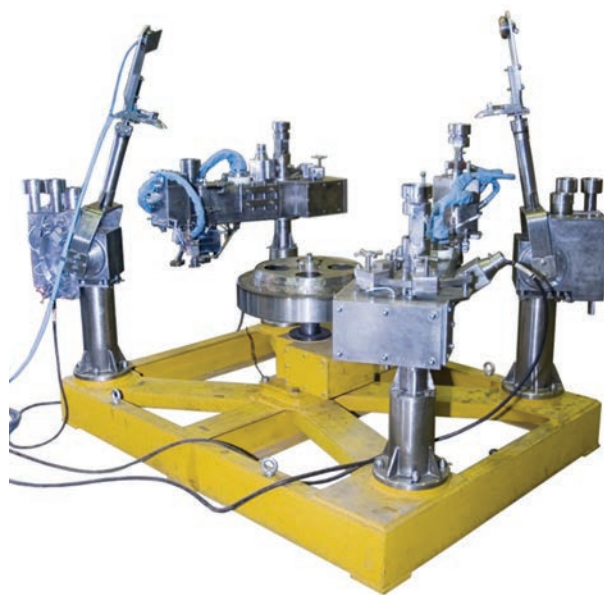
Установка контроля герметичности сварных соединений пеналов после загрузки в них ОЯТ
